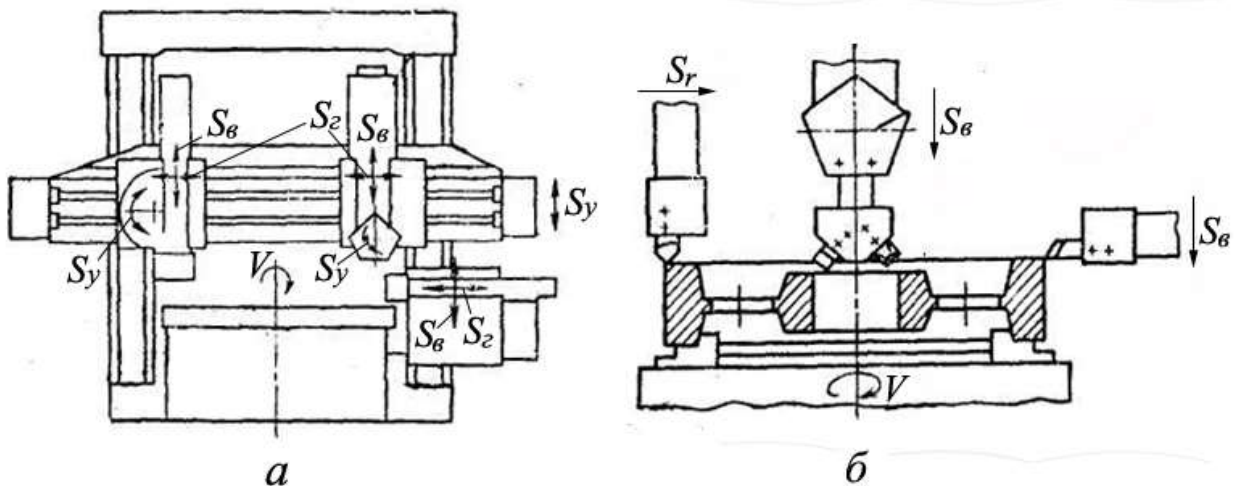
Загальний вигляд (а) і схема обробки заготовки (б) на карусельному верстаті
